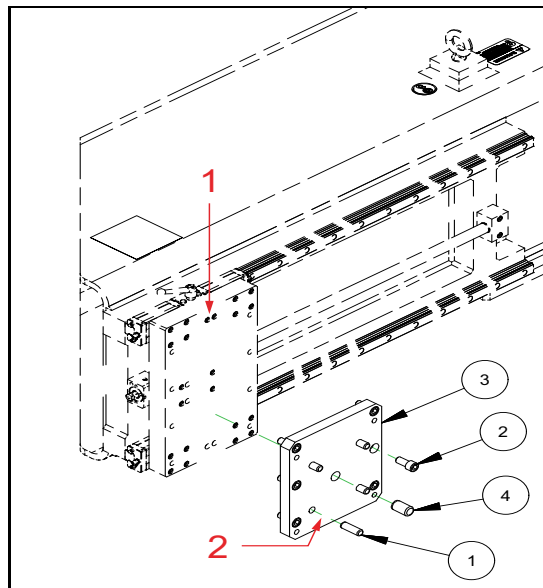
PLAQUE À GLISSIÈRE LATÉRALE
